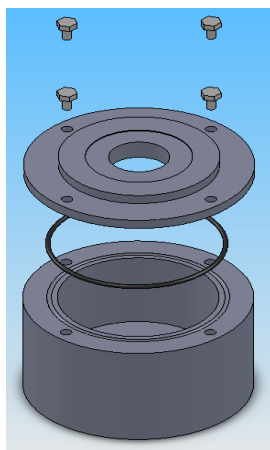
Vista explodida da nova coquilha de alumínio projetada em SolidWorks.
